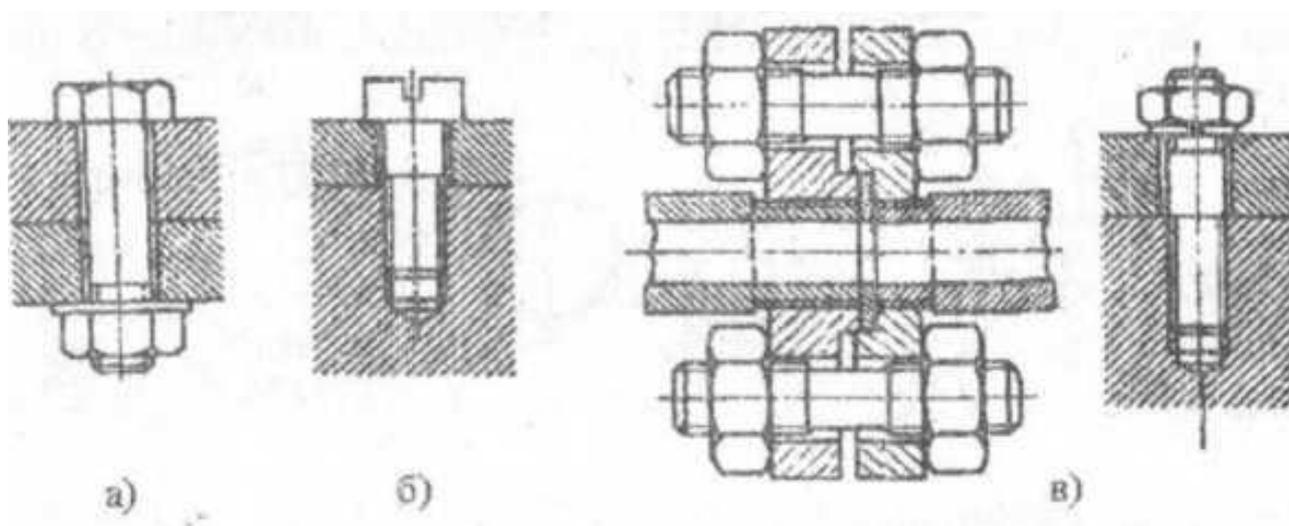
Резьбовые соединения деталей: а - болтовое; б - винтовое; в — шпилечное
